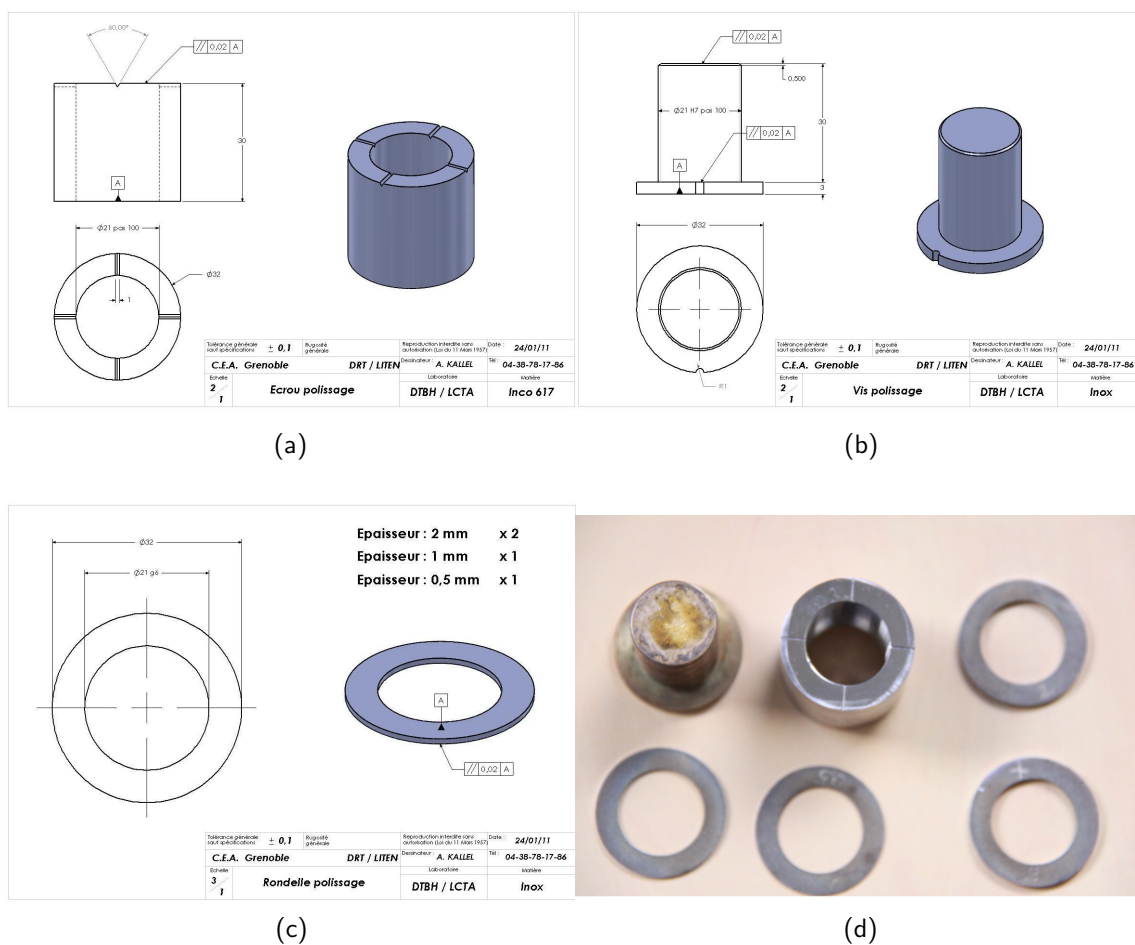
a, b, c : dessins de définition du dispositif de polissage et d :vue d'ensemble du porte échantillon de polissage
